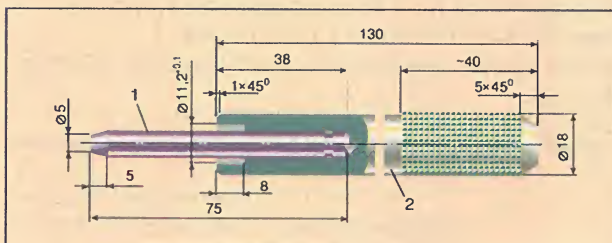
Оправка для запрессовки направляющей втулки клапана двигателя на автомобилях ВАЗ, ЗАЗ: 1 – стержень от изношенного клапана; 2 – оправка.
